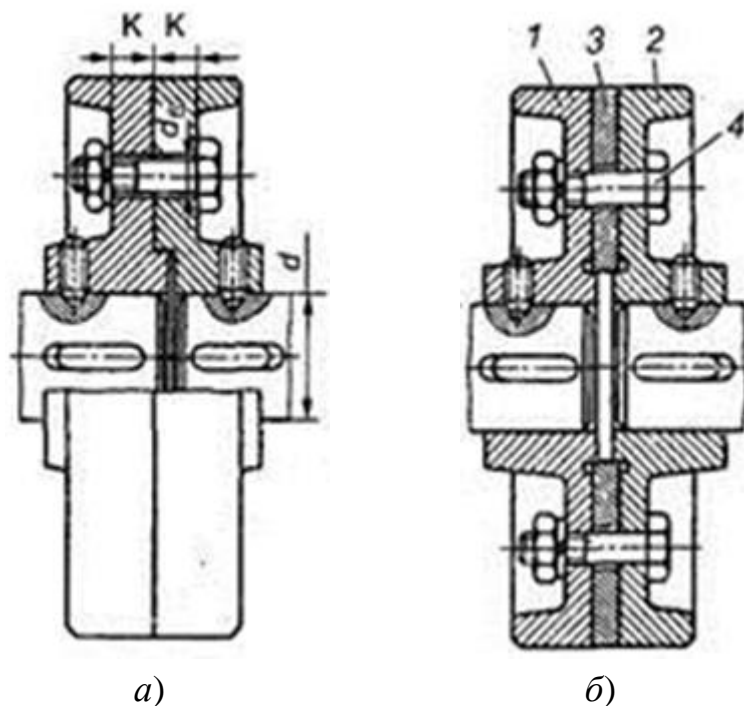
Фланцевые муфты: а - центровка за счет выступа; б — центровка кольцом
